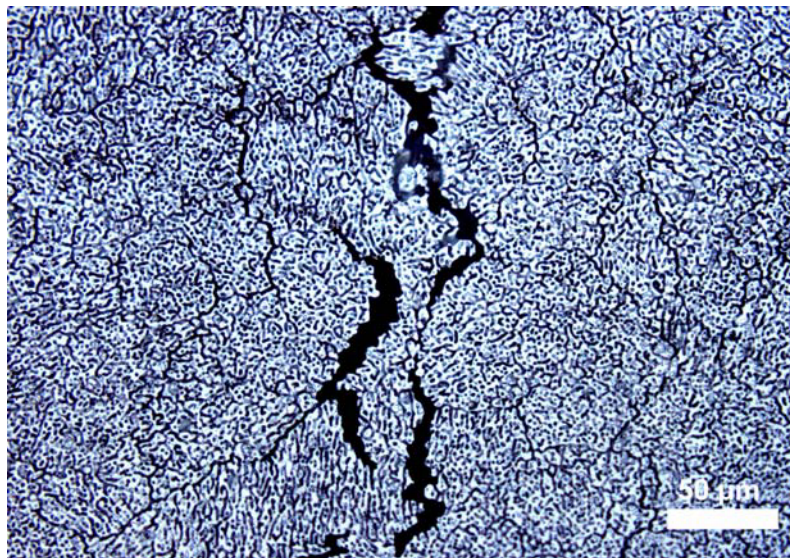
fissure branchée en coupe longitudinale dans une soudure bord à bord
